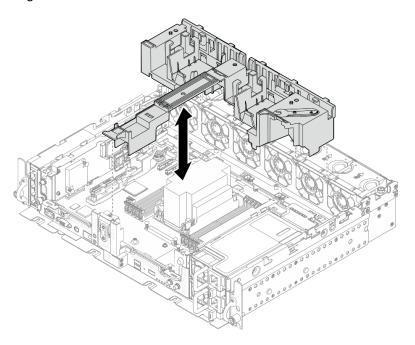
Removendo o defletor de ar de 360 mm com adaptadores de comprimento integral
